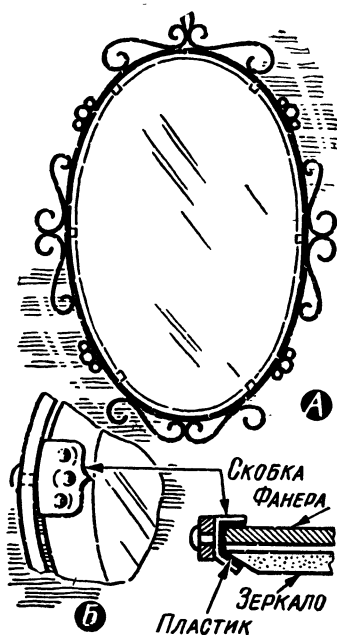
Зеркало: А — общий вид; Б. — крепление.
